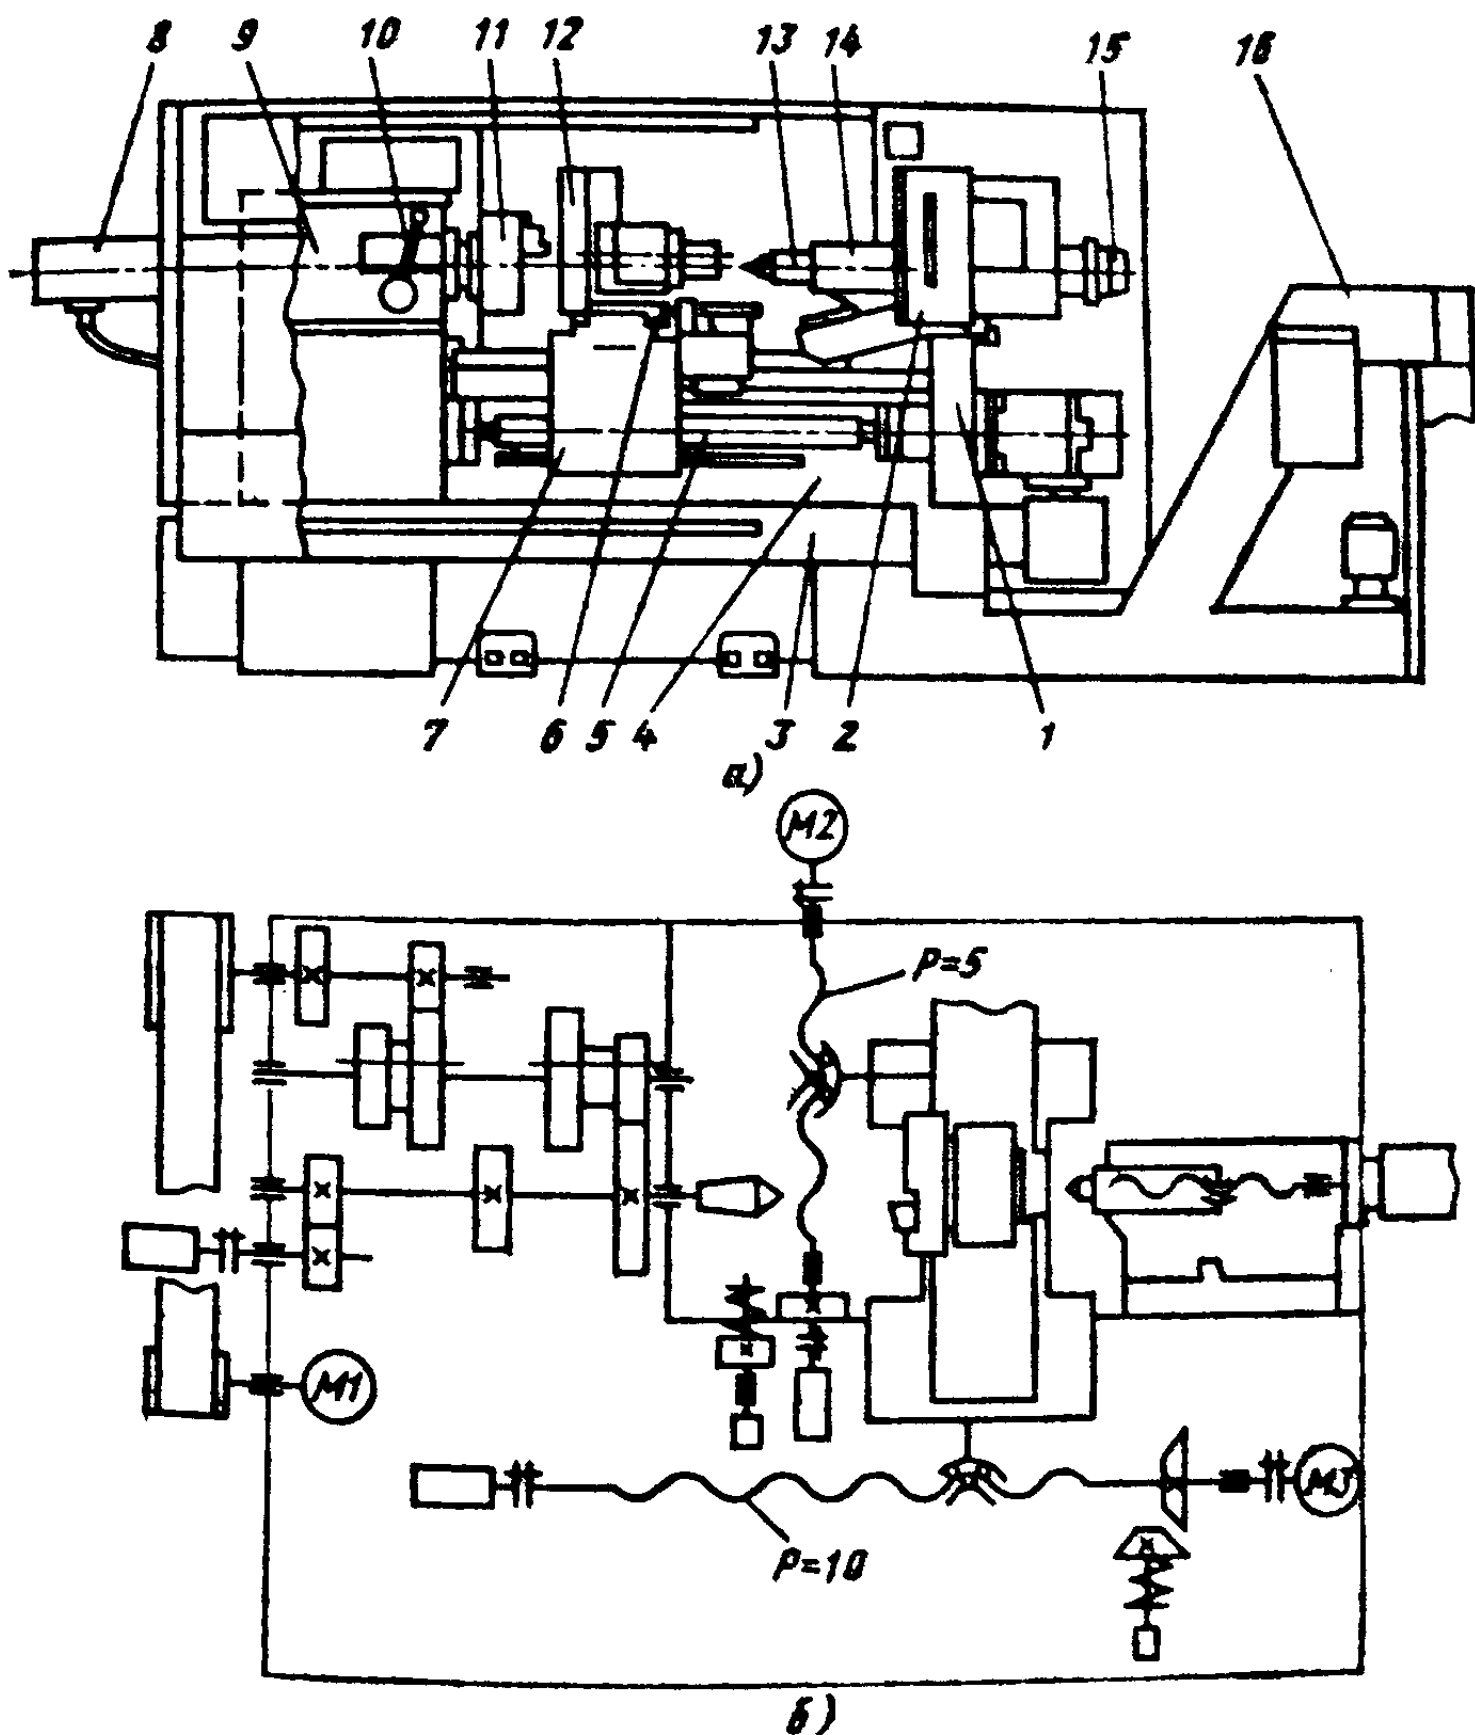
Общий вид (а) и кинематическая схема (б) токарного станка с ЧПУ
